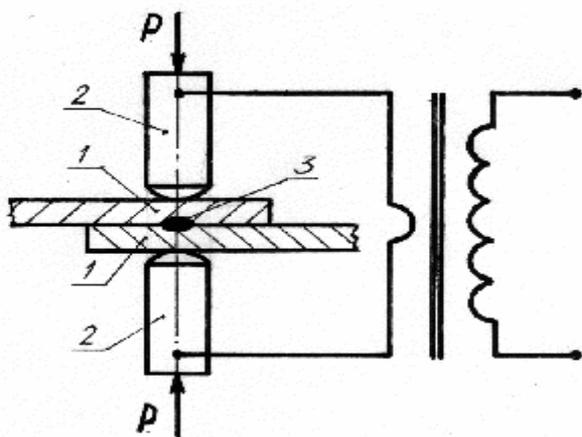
Схема контактной точечной сварки: 1 – заготовка; 2 – электрод; 3 – сварная точка
